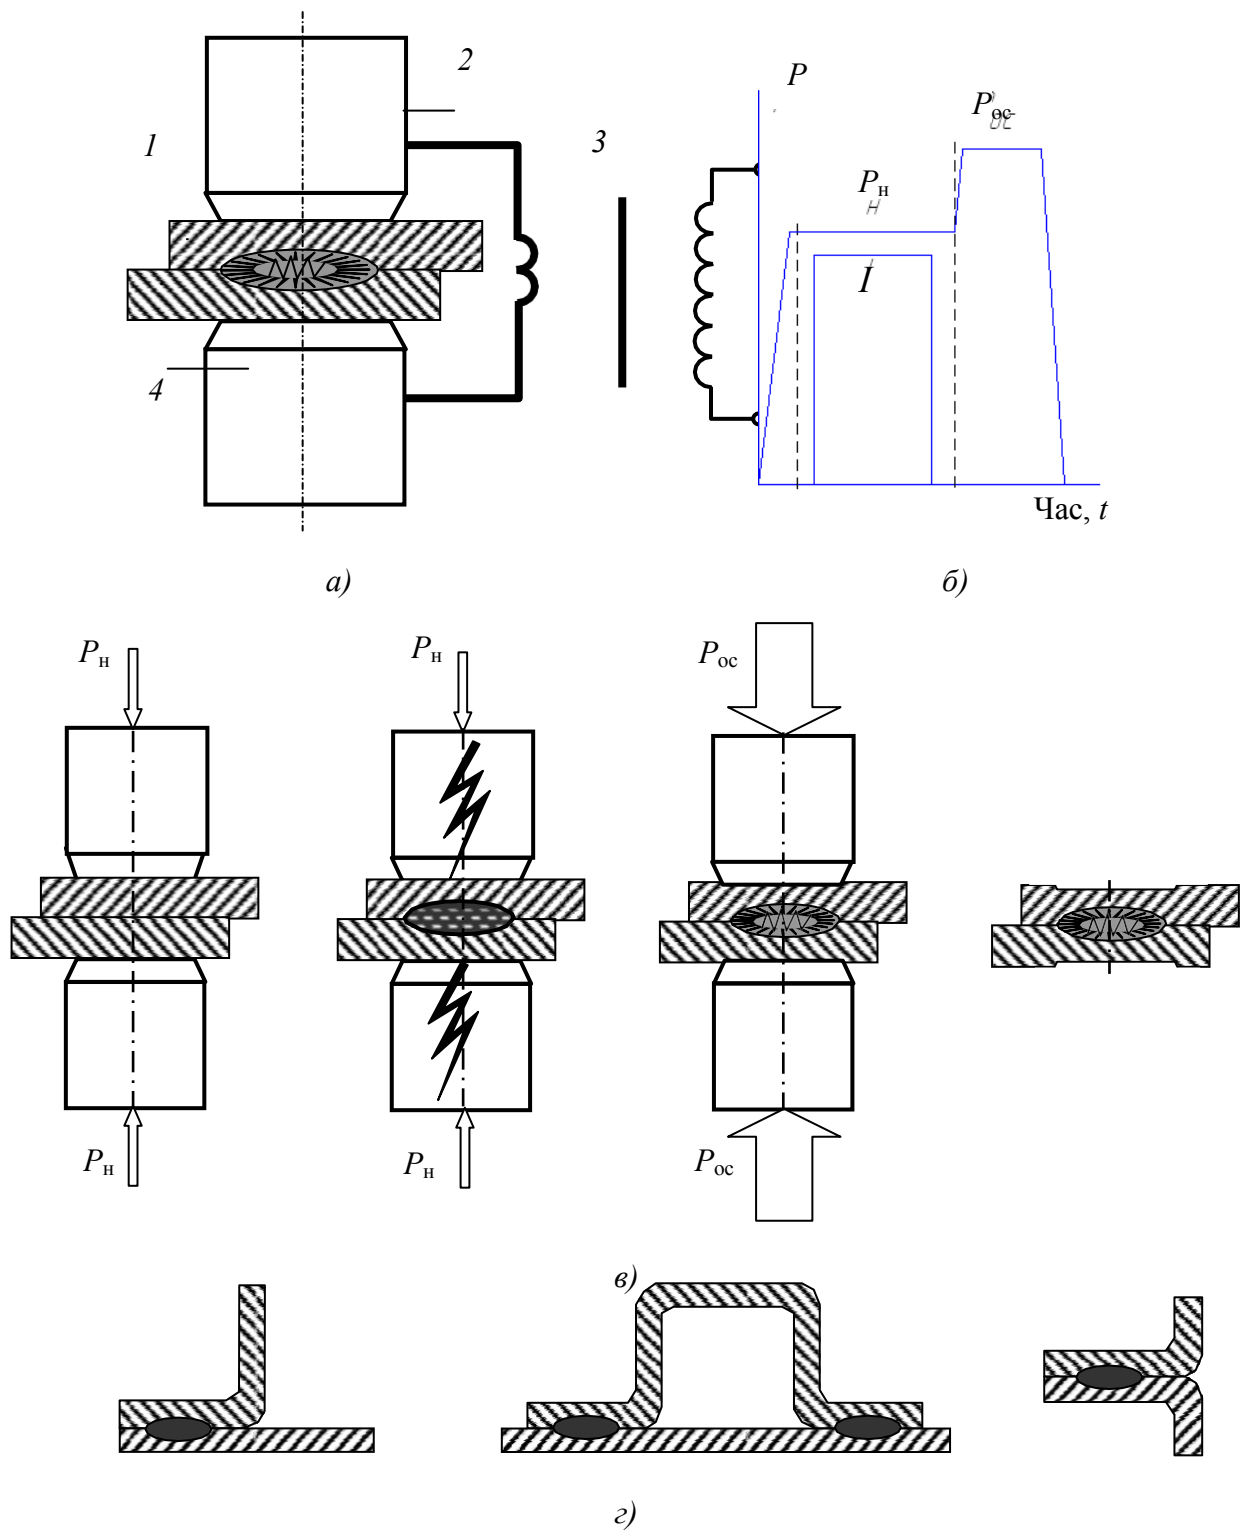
Точкове контактне зварювання: а) – схема зварювання; б) – циклограма; в) – стадії зварювання; г) – типи зварних з'єднань
